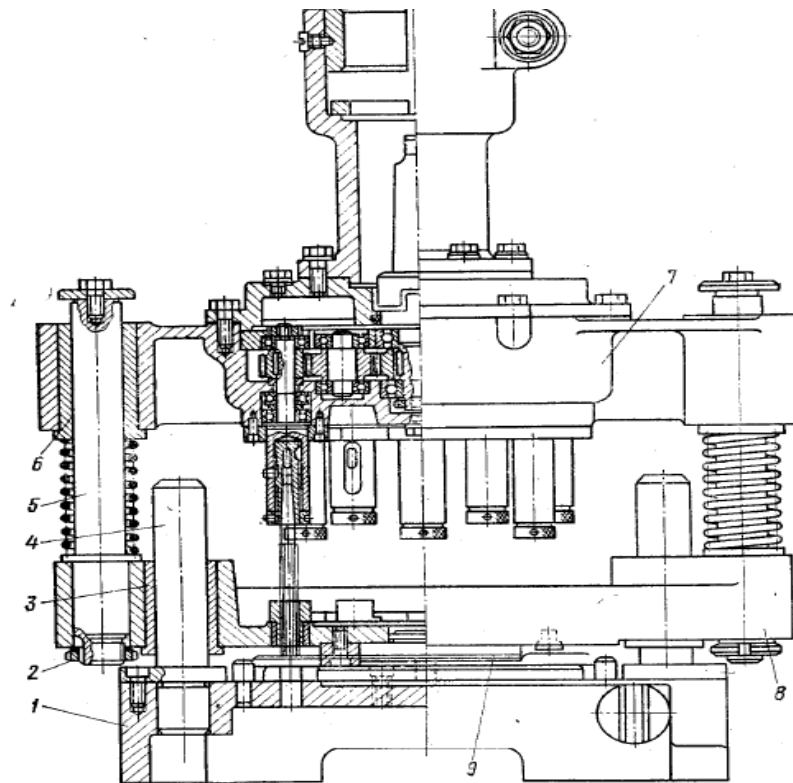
Багатошпіндельна свердлильна головка з підвісною кондукторною плитою
